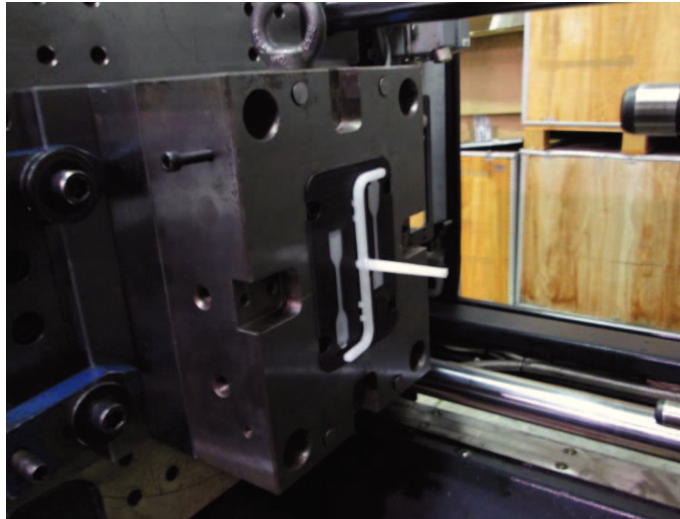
Injeção de PP sobre molde com superfícies moldantes em PA66 GF30
